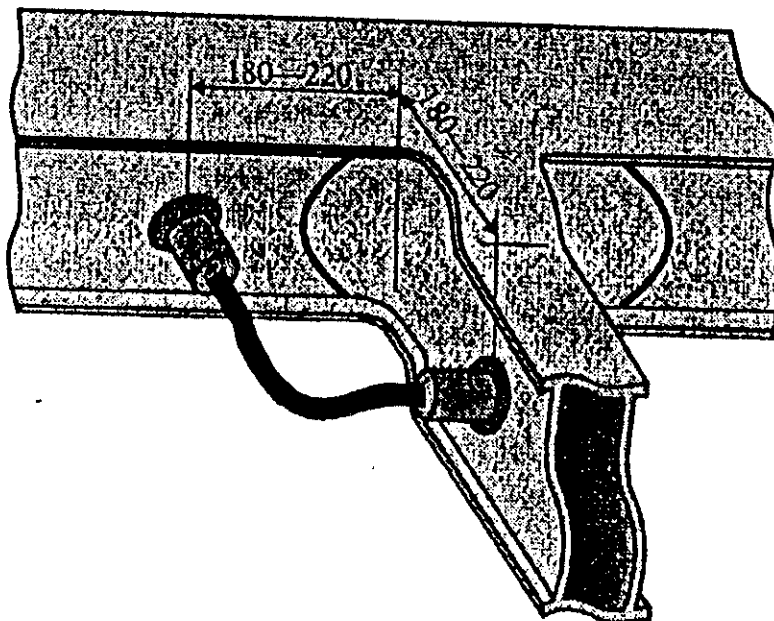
Намагничивание перехода от продольной балки к поперечной
